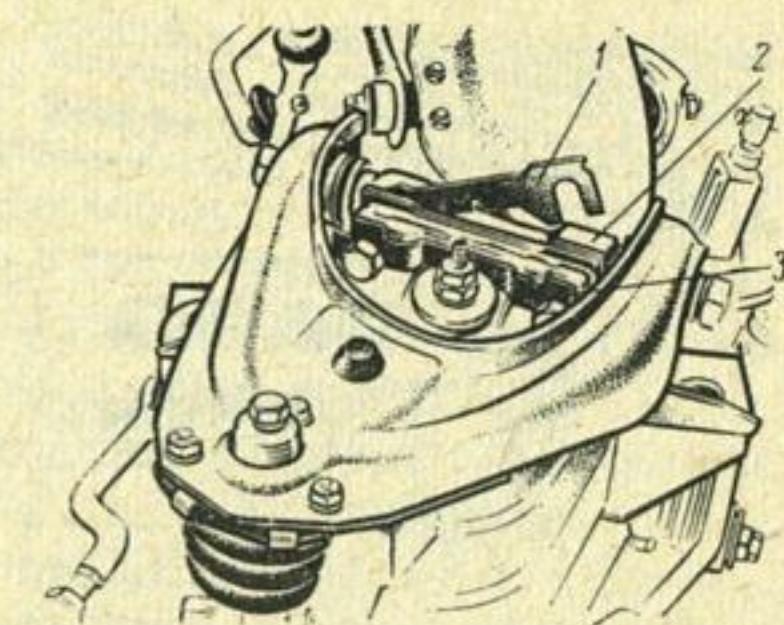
Узел регулировки поперечного угла наклона стойки (развала колес)
